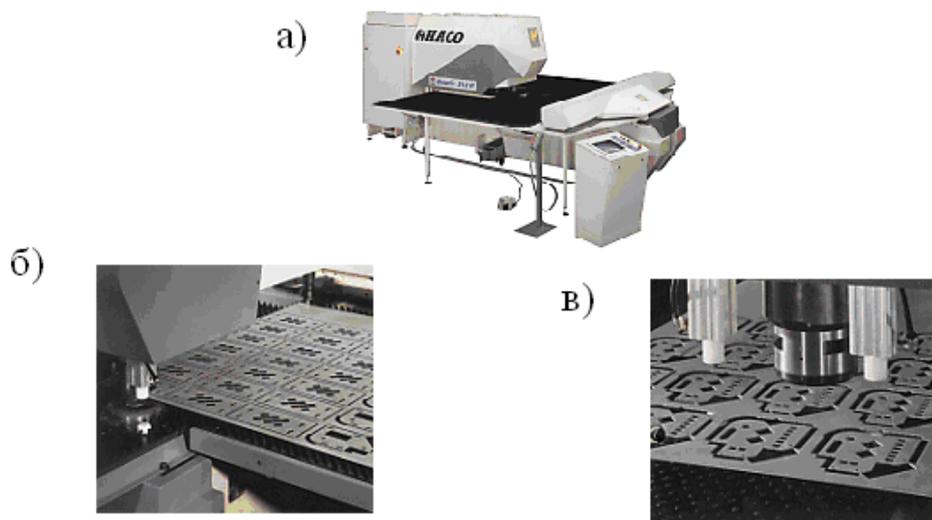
Гидравлический координатно-револьверный пробивочный пресс с ЧПУ фирмы НАСО (Бельгия) модели Omatic 212 RH и образцы пробивки на прессе
